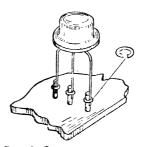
Способ креплення выводов деталей на опорных шпильках.
